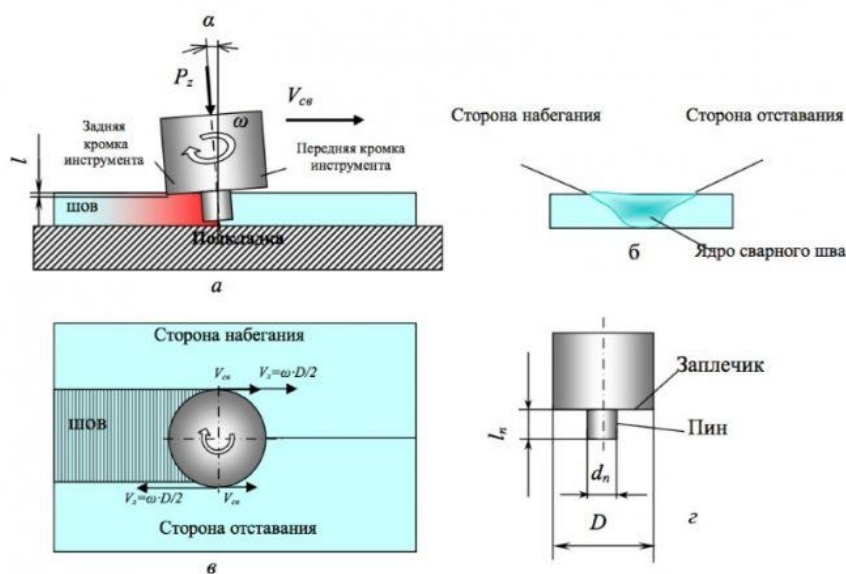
Схема процесса сварки трением с перемешиванием
